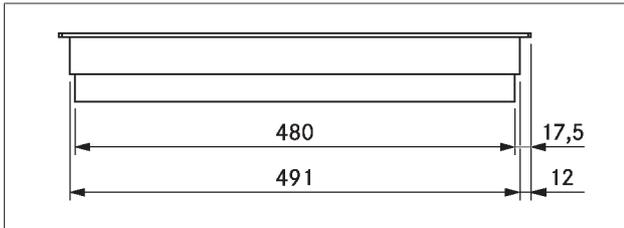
CKCB Gerätemaße Seitenansicht
